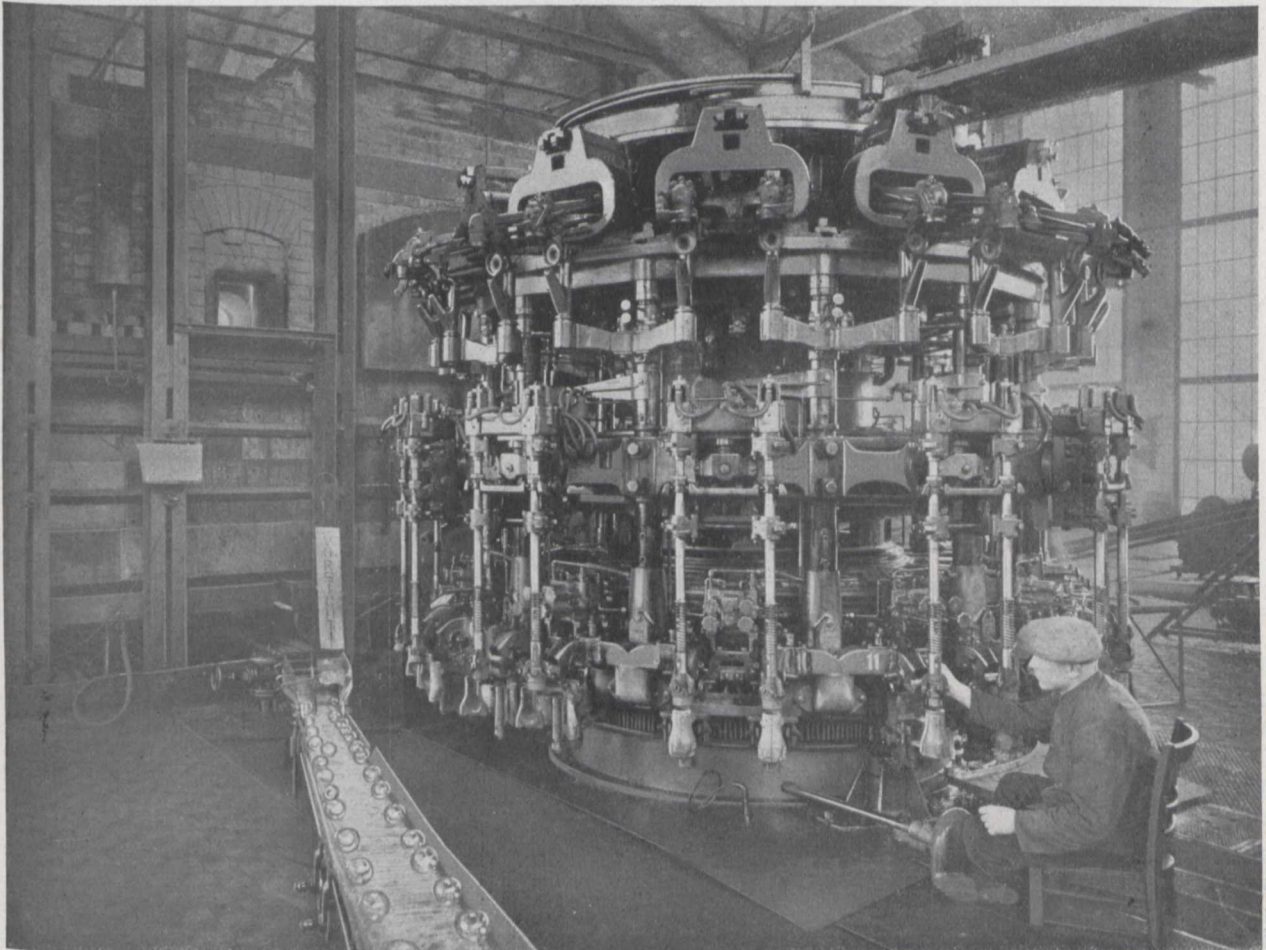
Kolbenblasmaschine, die täglich 50000 Glühlampenkolben herstellt.
